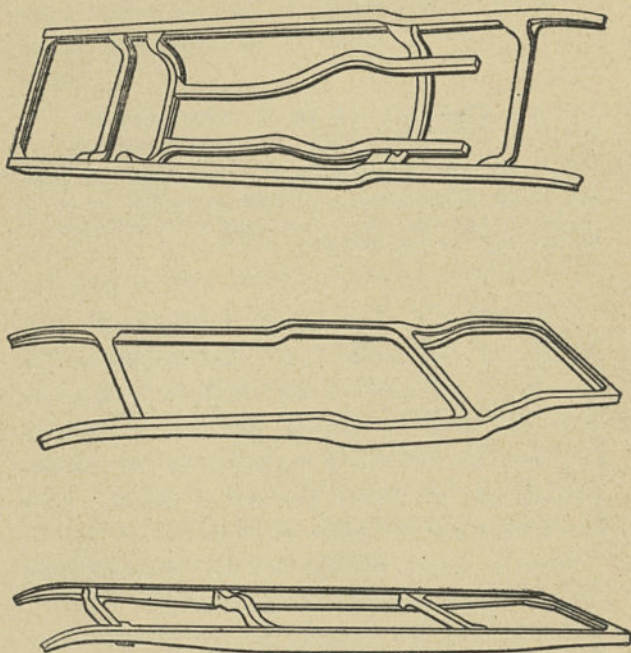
, 12, 13. — Spécimens de châssis en tôle emboutie.
